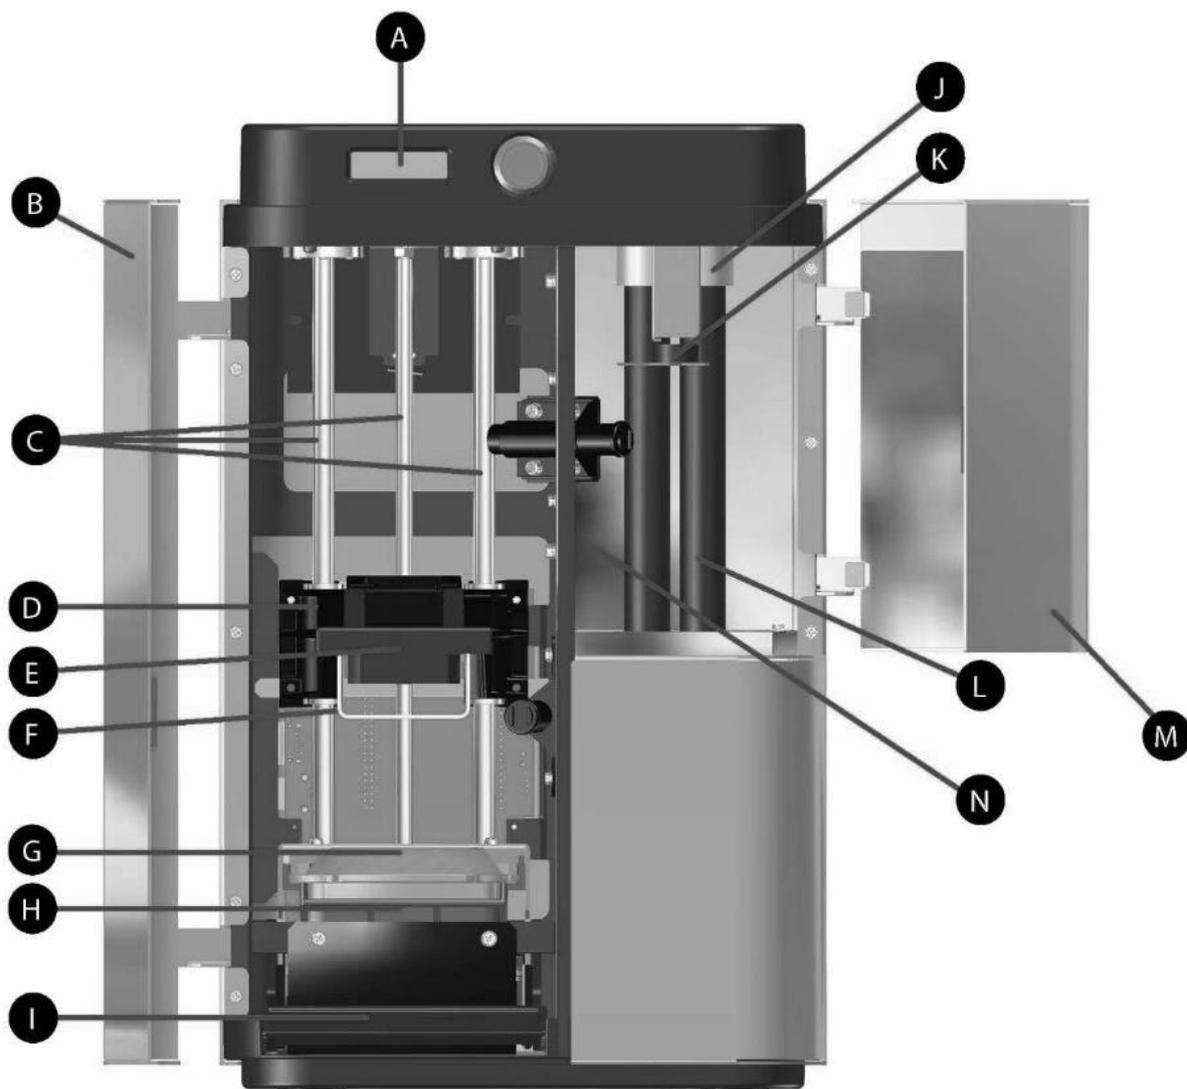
Внешний вид 3-D принтера ProJet 1200
